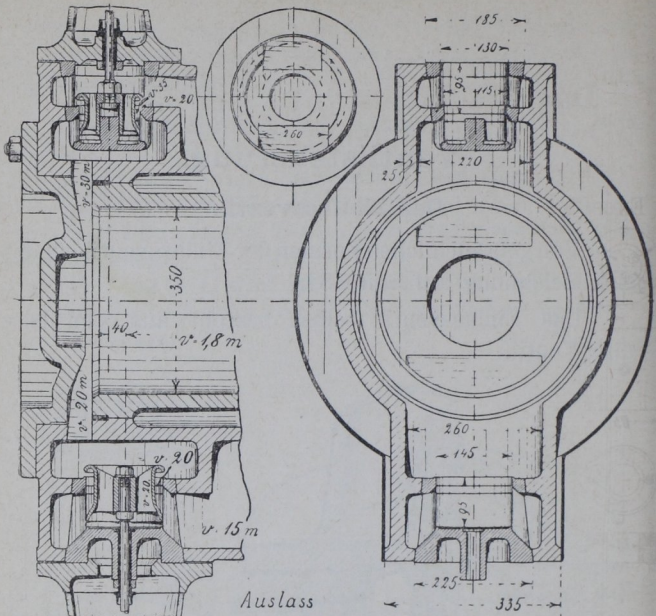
402. Ventilsteuerung für 350 mm Cylinderdurchmesser.
